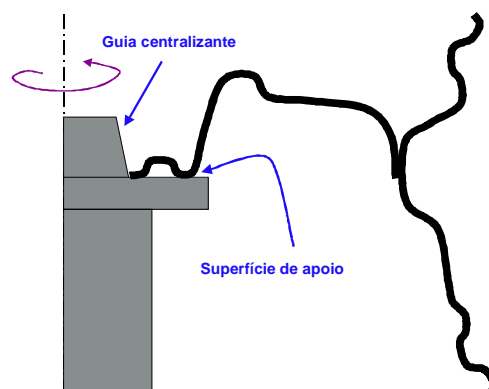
Esquema do dispositivo de posicionamento da roda para inspeção de oscilação
